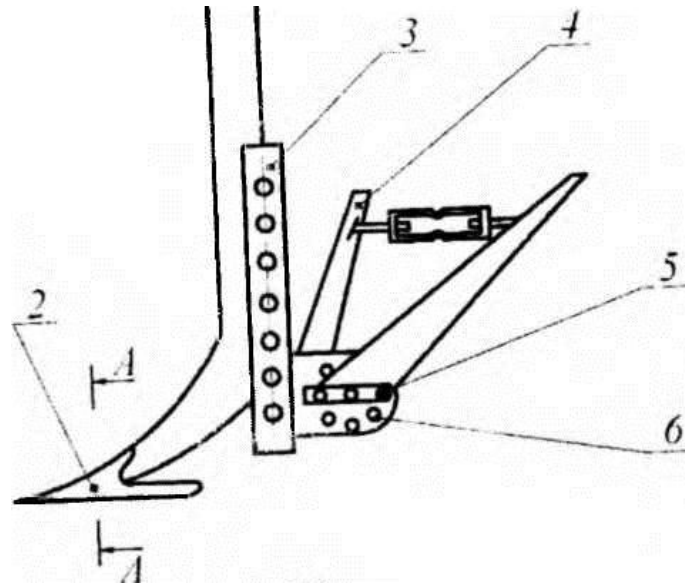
Робочий орган для міжрядного обробітку ґрунту, [12], вид збоку
